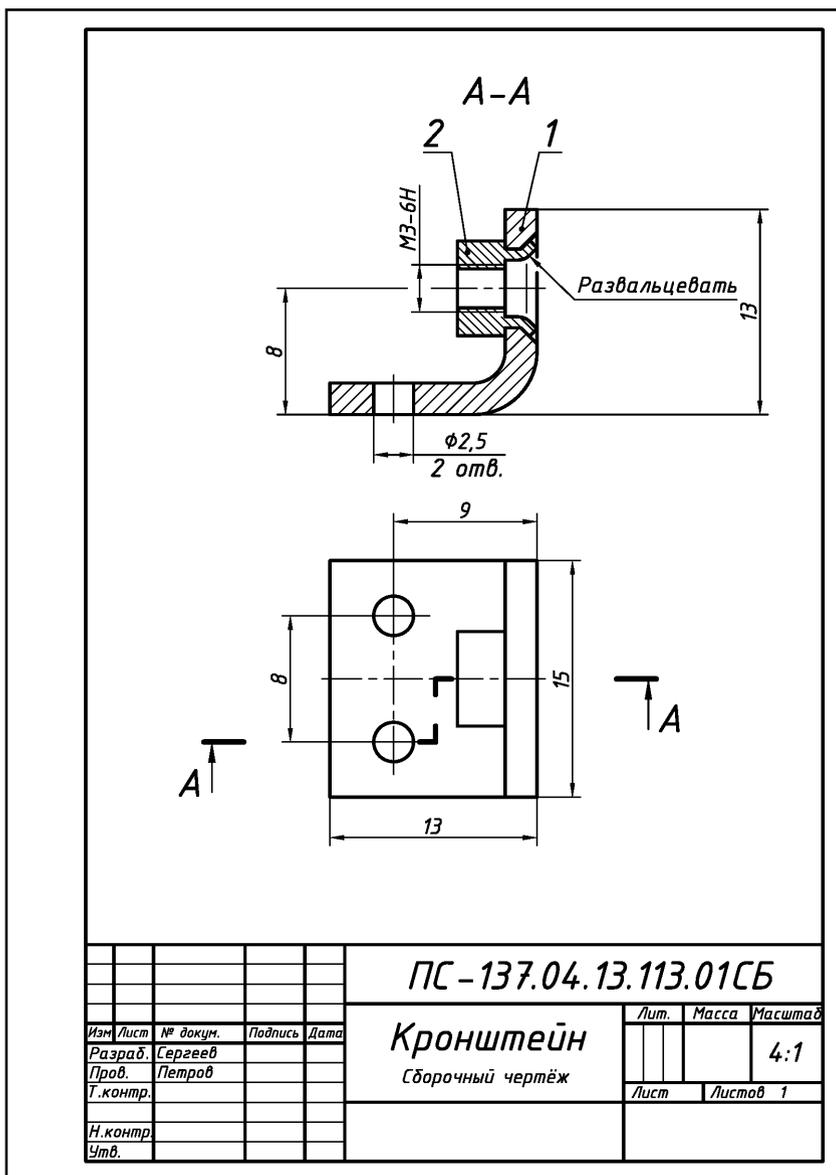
Оформление рабочего чертежа сборочной единицы «Кронштейн», образованной развальцовкой
